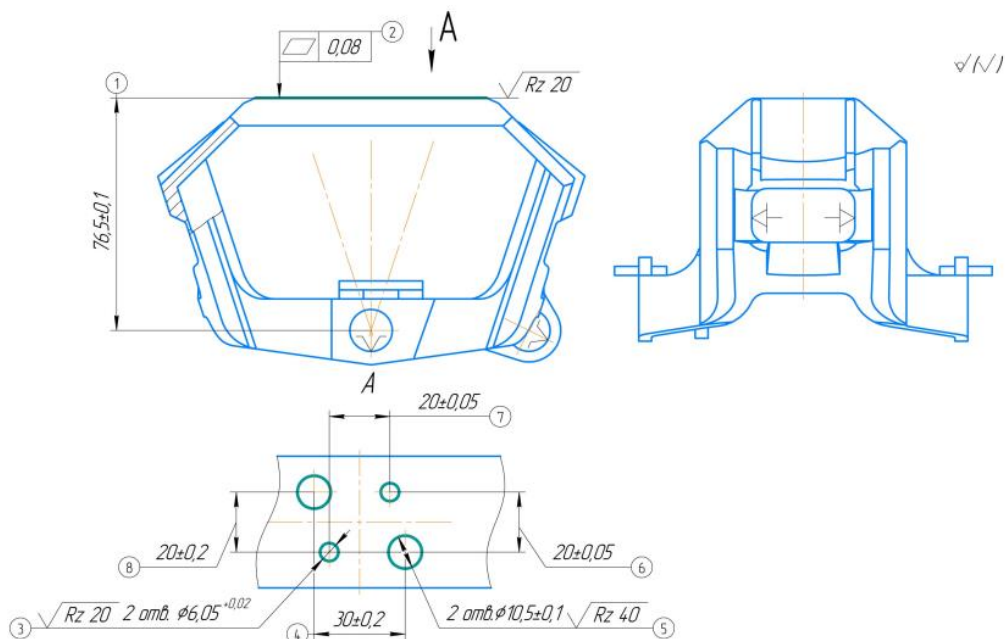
Эскиз к операции 045 – Фрезерная с ЧПУ
